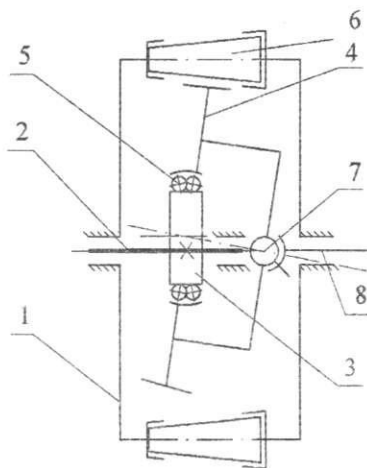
Структурная схема ППП с зубьями сателлита, имеющими профиль зубьев звездочки цепной передачи:
